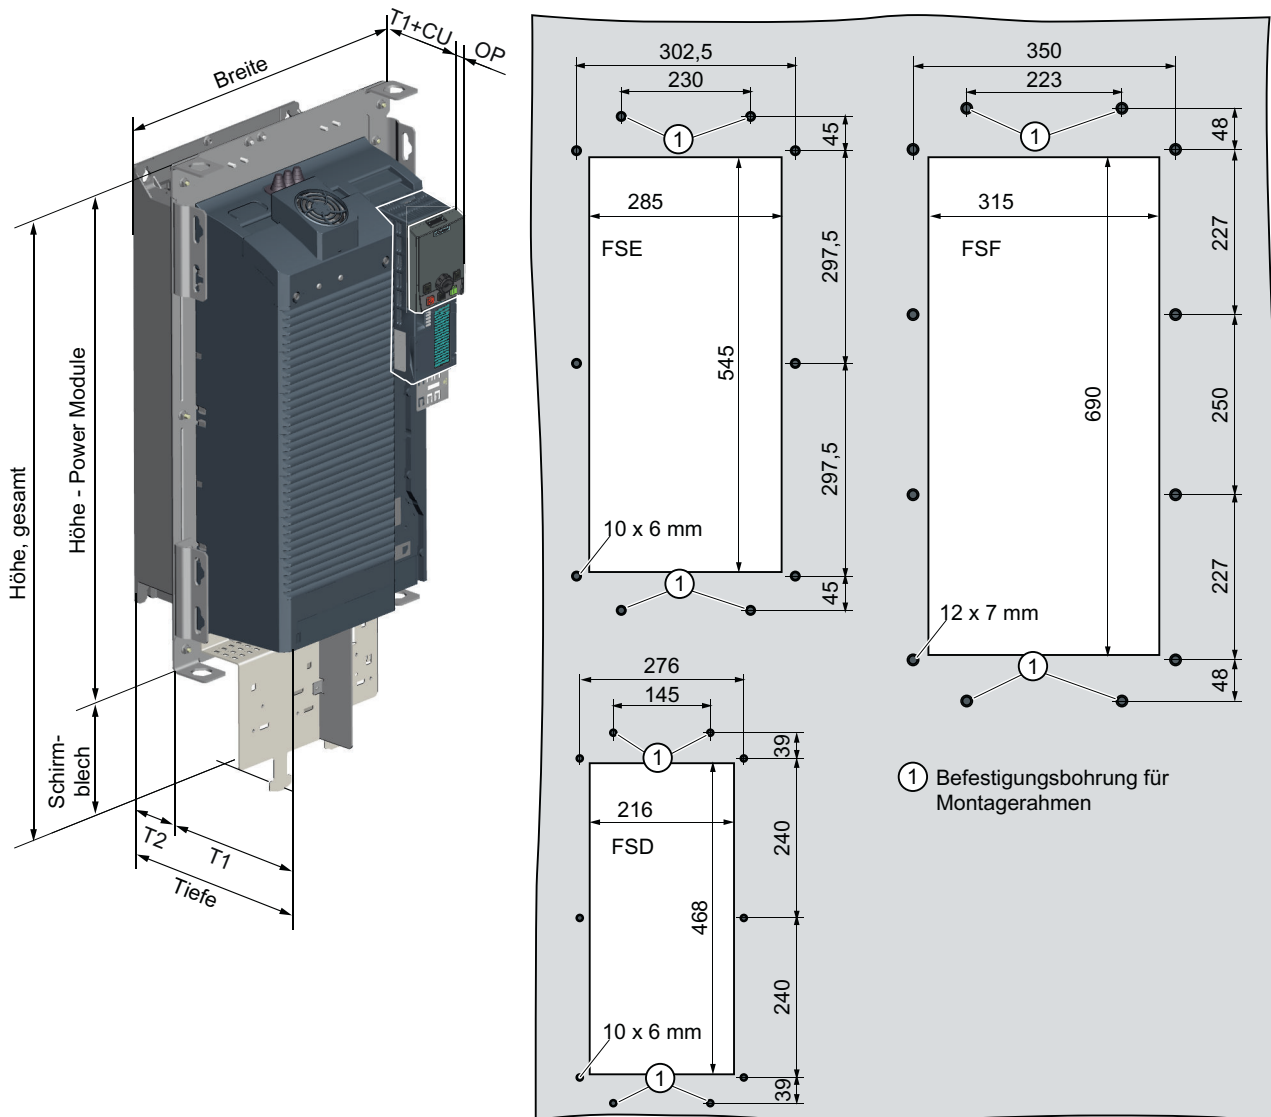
Maßbild und Bohrmaße für die Baugrößen FSD ... FSF
